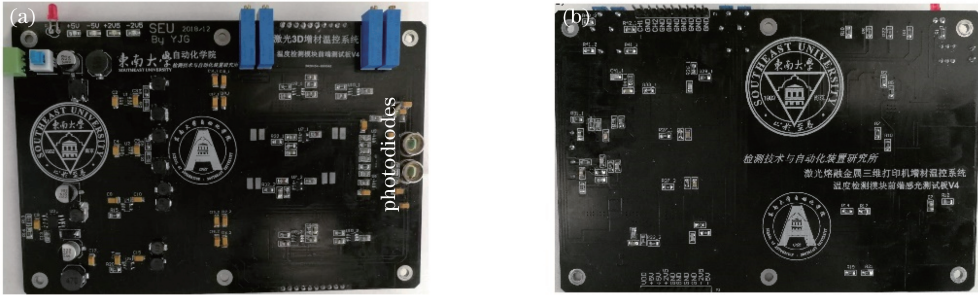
光电检测 PCB 实物图。(a)正面;(b)反面
